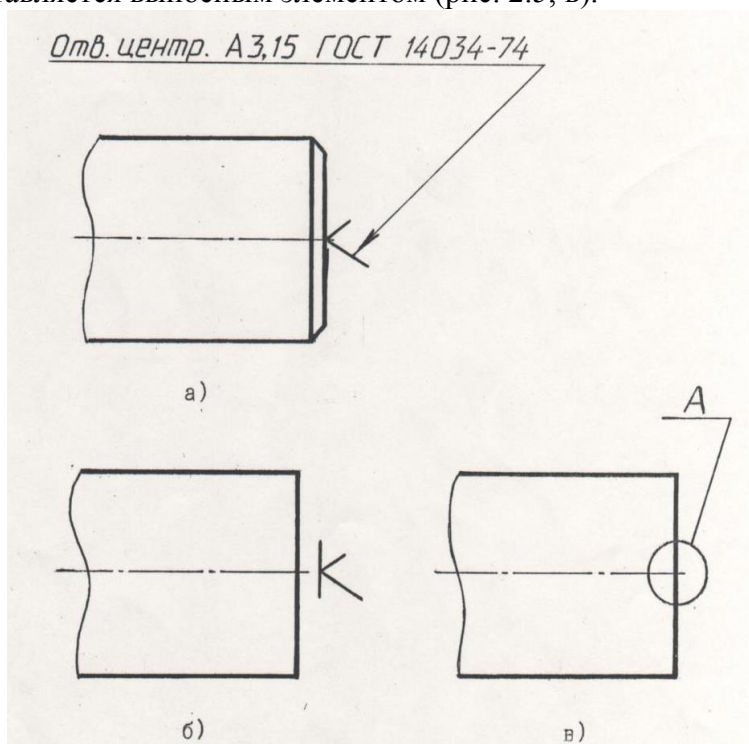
Обозначение центровых отверстий на чертежах.
